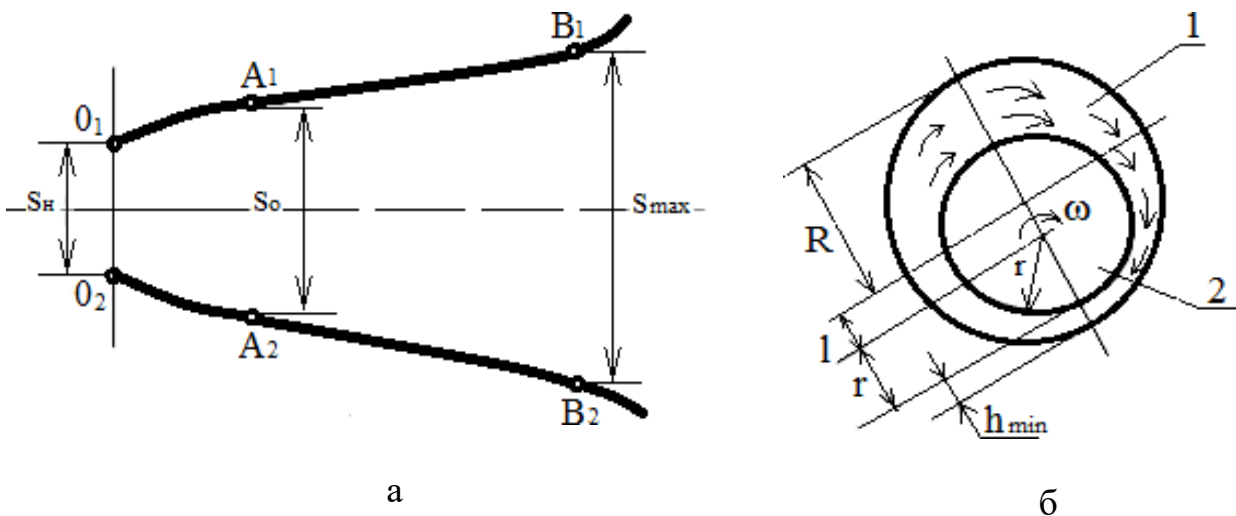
Схема процесу зношування пари «вал-підшипник»:
